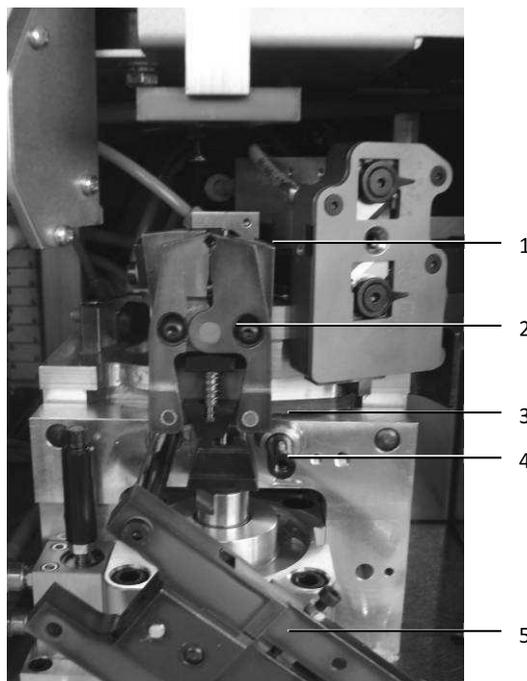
Hülsenhaltezange und Crimpwerkzeug
